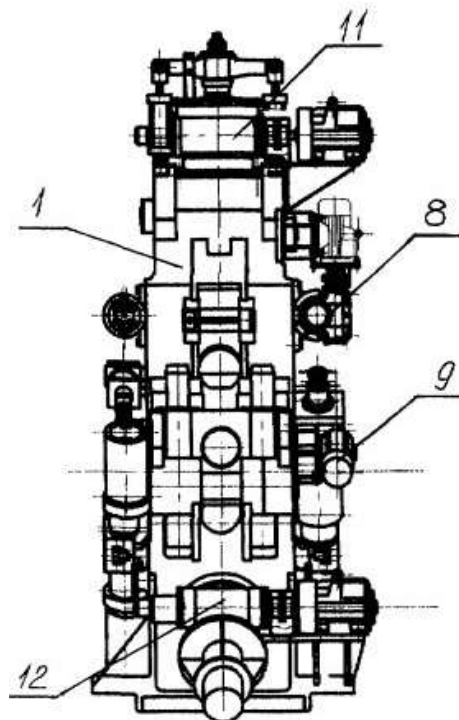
Рабочая клеть стана поперечно винтовой прокатки. Вид сбоку
